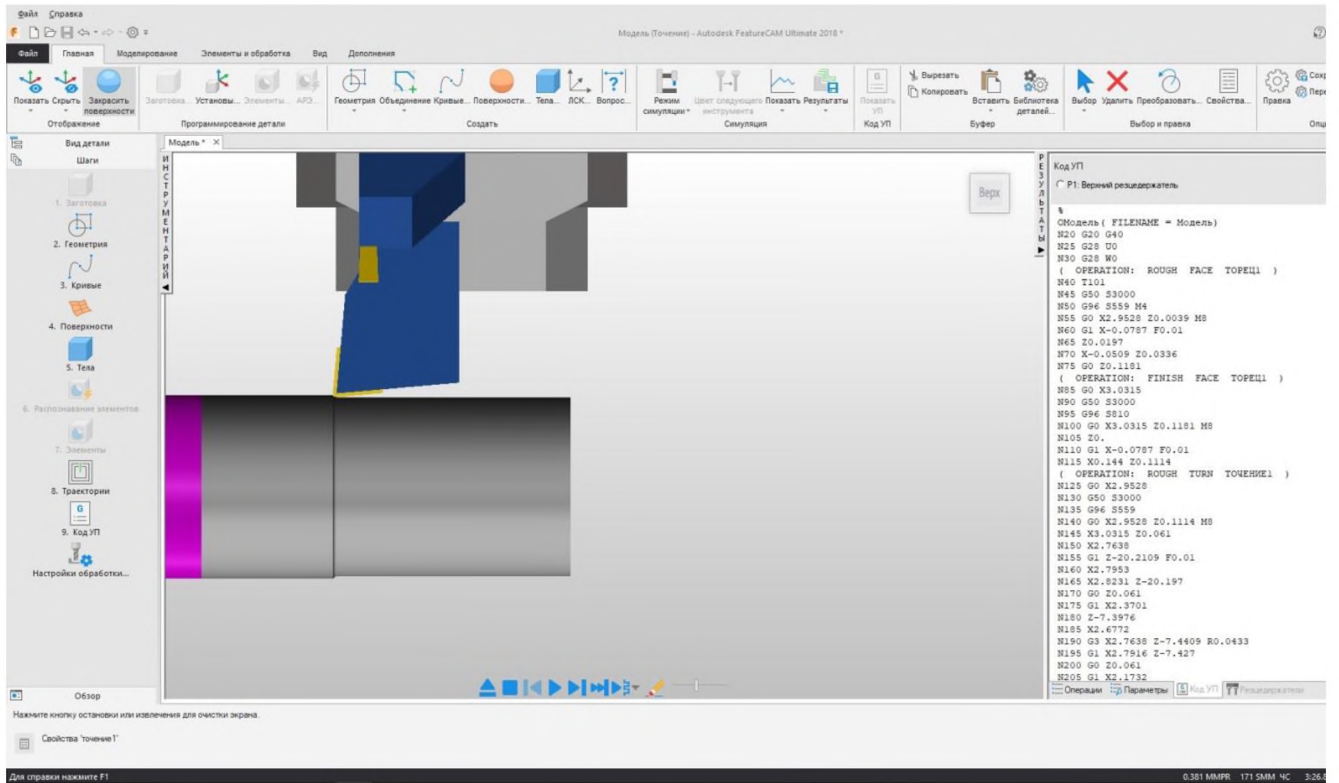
Моделювання процесу обробки деталі «Вал шліцьовий» – точіння (чорнове) циліндричної поверхні
